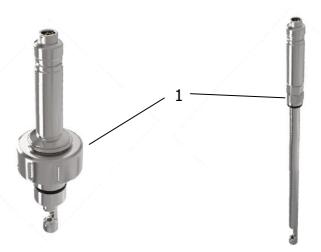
Überwurfmutter / Druckschraube am Sensor
